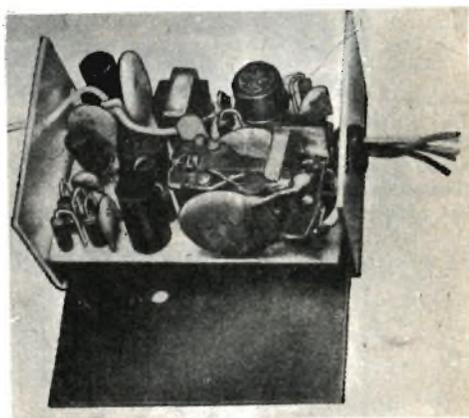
Per schermarlo al massimo da disturbi esterni, il circuito stampato del ricevitore deve essere racchiuso in una scatola metallica separata (sopra). Questa scatola si monta poi in una custodia più grande, sulla quale si devono fissare invece direttamente l'interruttore, la batteria e l'antenna.
